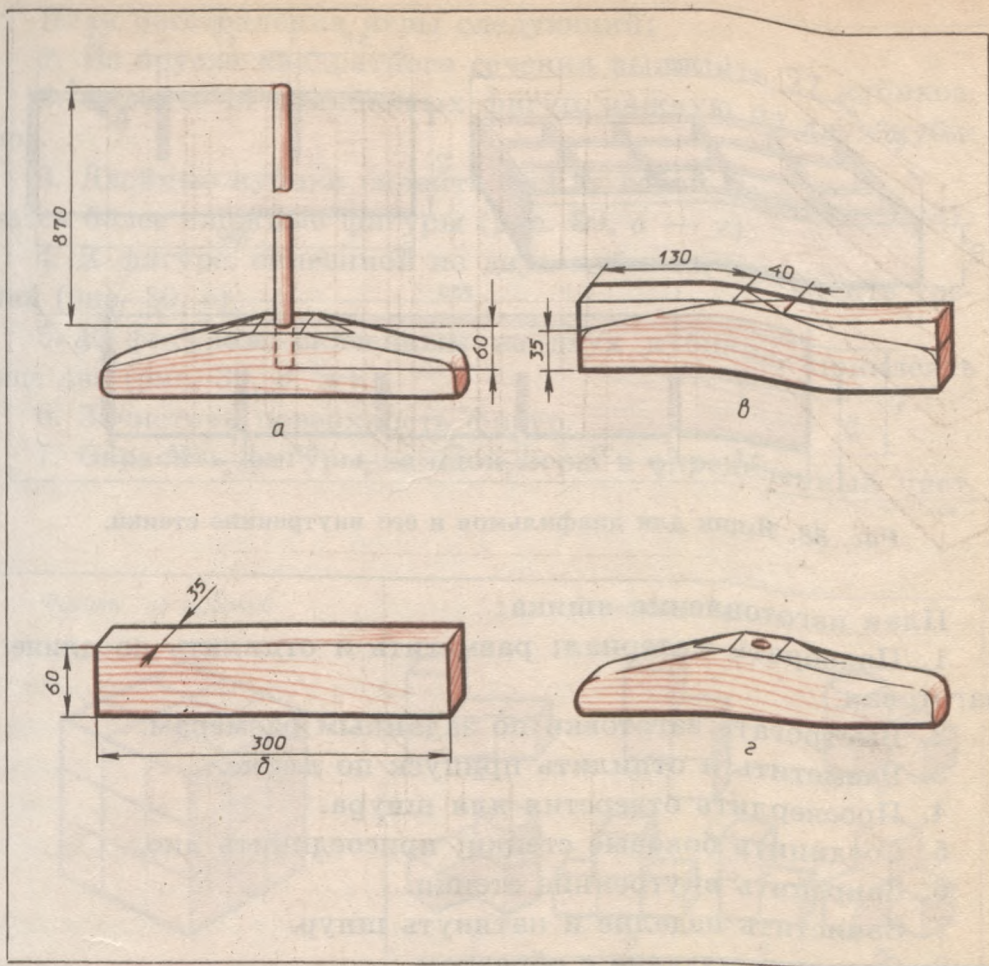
Швабра: а — готовое изделие; б — заготовка для колодки; в — размеченная заготовка; г — колодка.
